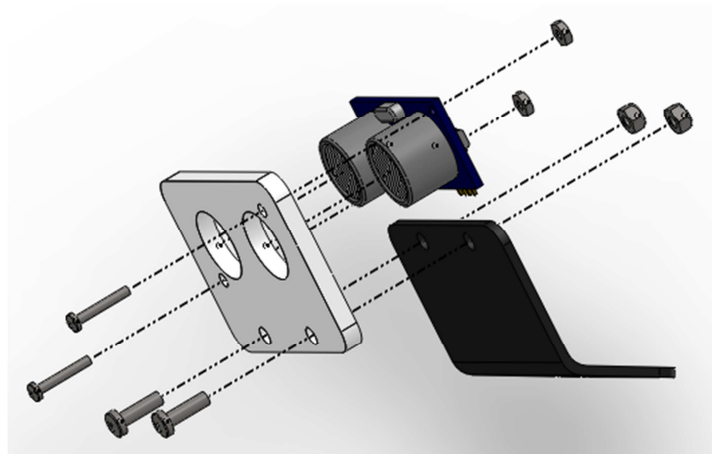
Vista explosionada del montaje de los sensores delanteros.
